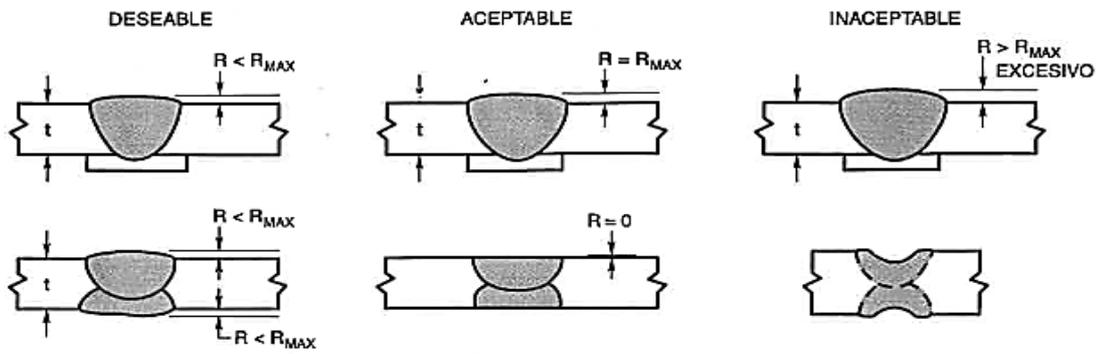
Perfiles de soldadura en junta a tope (ver tabla 4).
